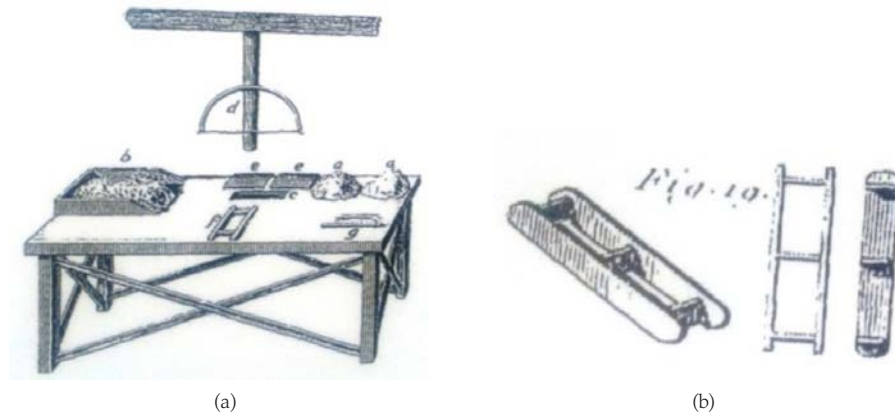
(a) Mesa do moldador; (b) Moldes duplos.
